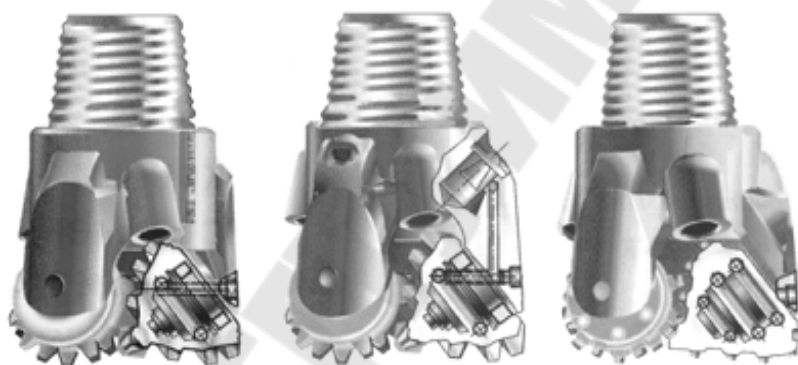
Конструктивные схемы трехшарошечных долот с боковой гидромониторной промывкой: а – с открытой опорой и фрезерованным вооружением; б – с герметизированной маслonaполненной опорой и фрезерованным вооружением; в – с открытой опорой и зубковым твердосплавным вооружением
